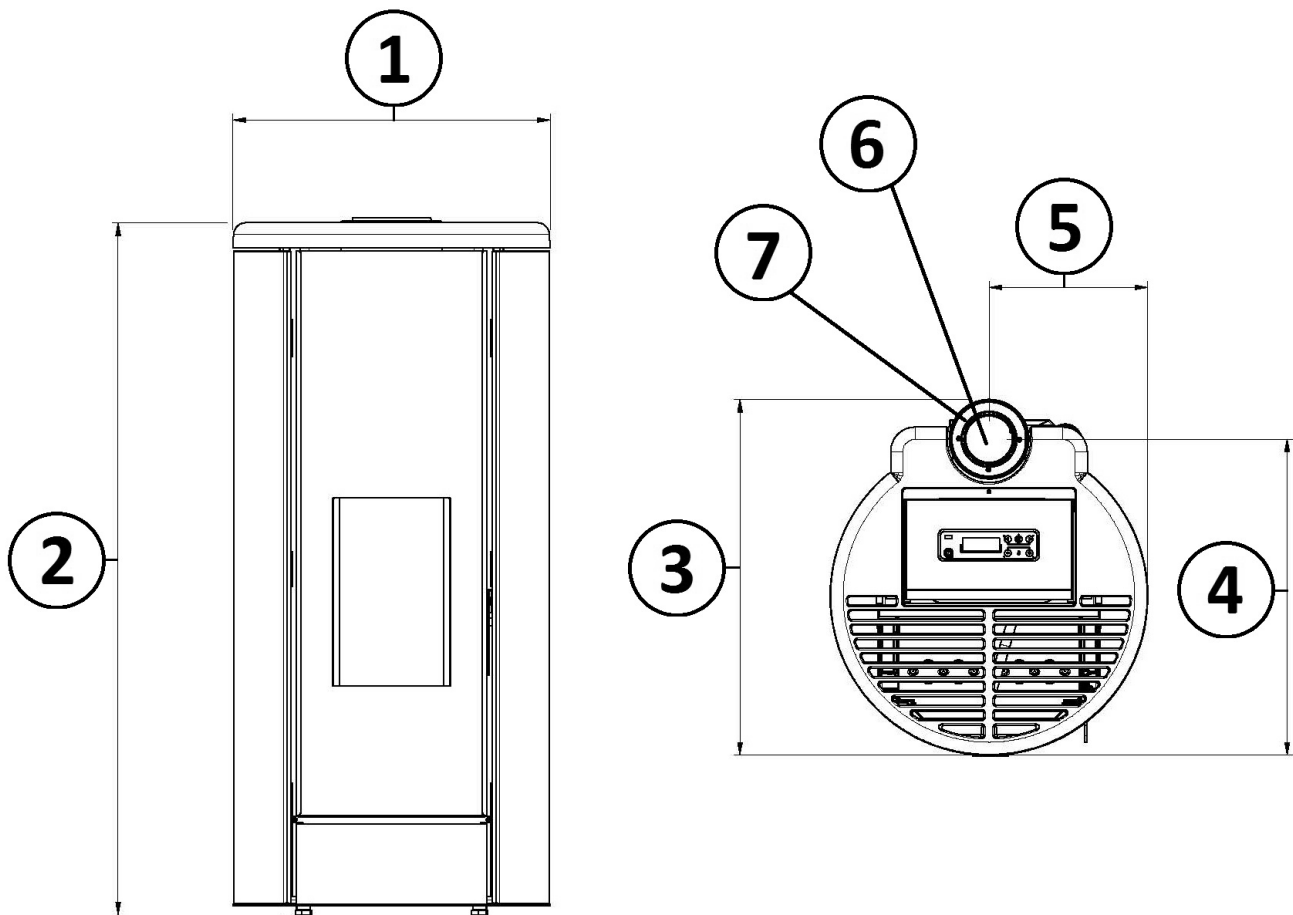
Algemene afmetingen: Titania Airtight - Venere Airtight
